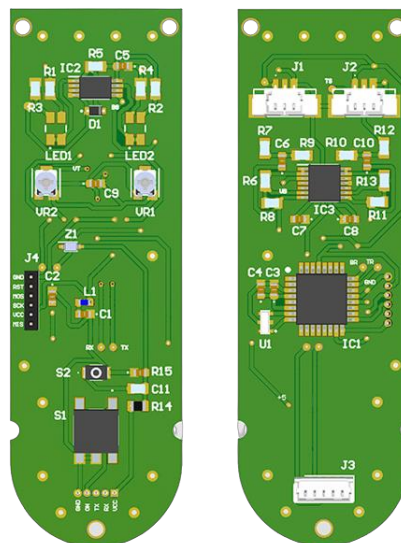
Diseño de PCB del módulo de adquisición instalado en manillar
